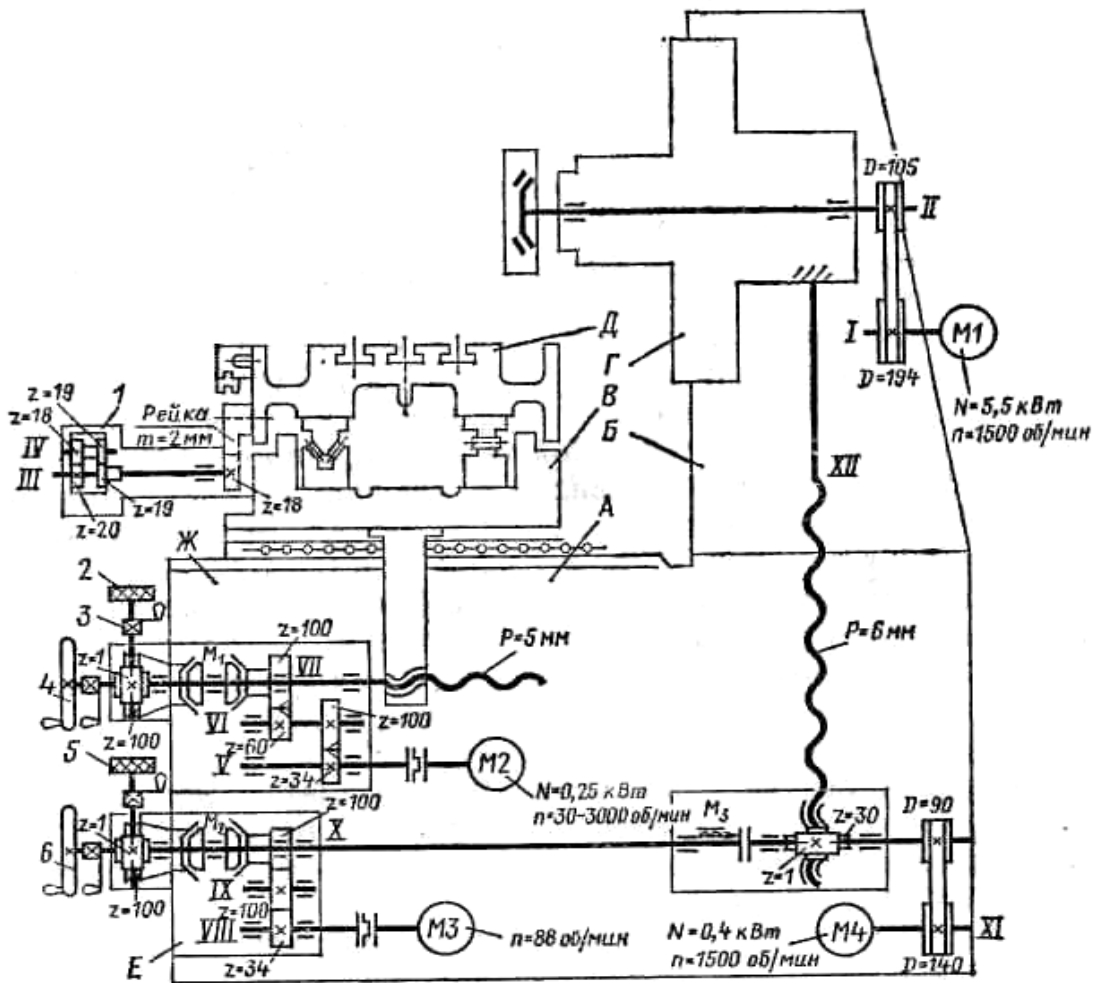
Кинематическая схема плоскошлифовального станка модели 3E711
